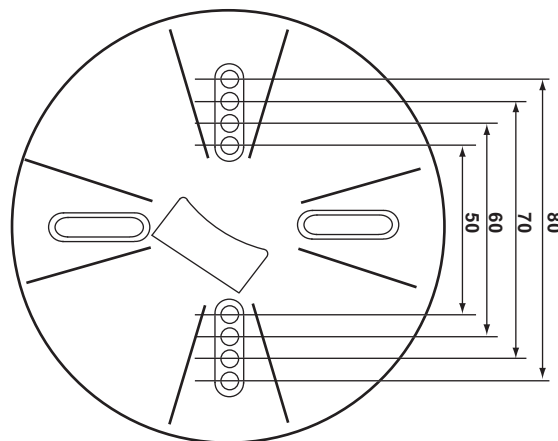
Flangia di montaggio— Dimensioni di fissaggio
